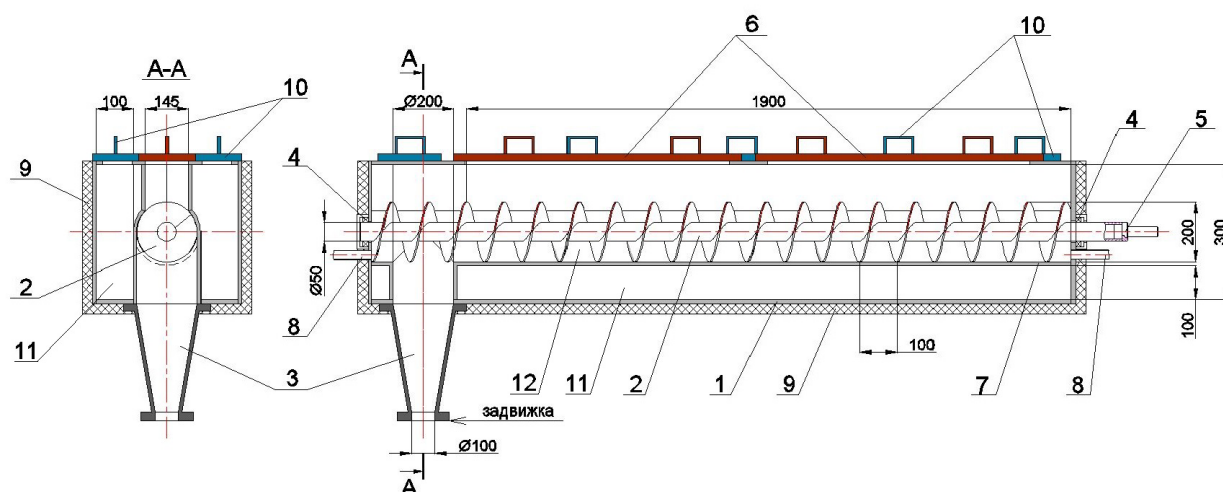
Эскиз устройства дозирования шквального града: 1 – корпус системы дозирования; 2 – шнек; 3 – конический трубопровод; 4 – опоры вала шнека; 5 – выходной вал шнека; 6 – крышки (используются для загрузки града); 7 – стенка, образующая полость для установки шнека; 8 – патрубки для прокачки охлаждённого осушенного воздуха через полость, образуемую шнеком; 9 – слой теплоизоляции; 10 – крышки для загрузки охлаждающей жидкости; 11 – полость для хладоносителя; 12 – место загрузки града
